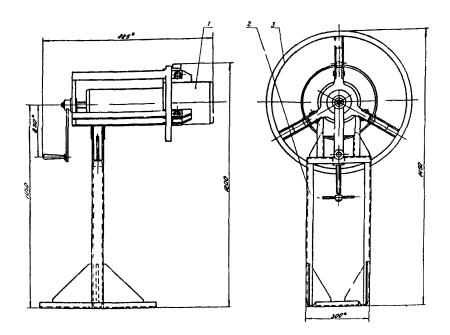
Приспособление пля снятия колеса и брони насоса ГрТ 1600/50 (сборочный чертеж):
